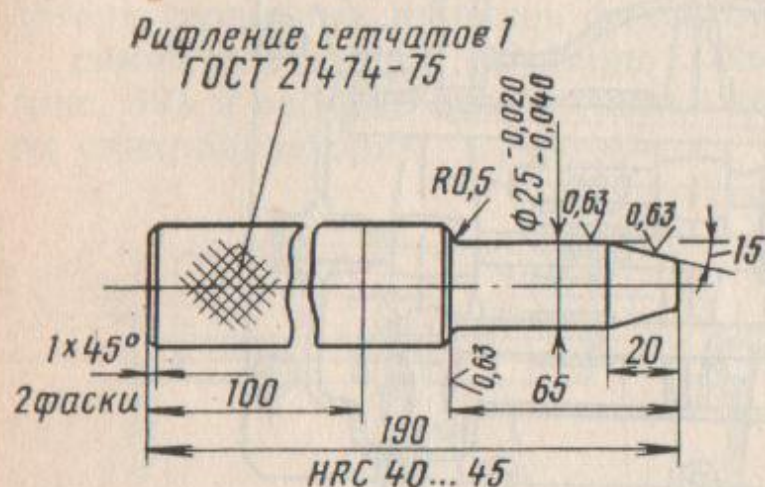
Оправка для установки штоков в корпус крышки коробки передач
